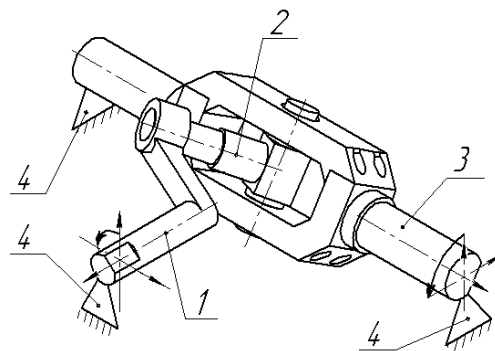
Просторовий шарнір: 1 – кривошип; 2 – шатун; 3 – коливальний вал; 4 – опора
